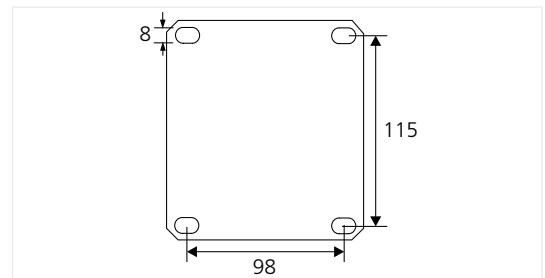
Abmessungen für Montagelöcher Montageplatte (Angaben in mm)
